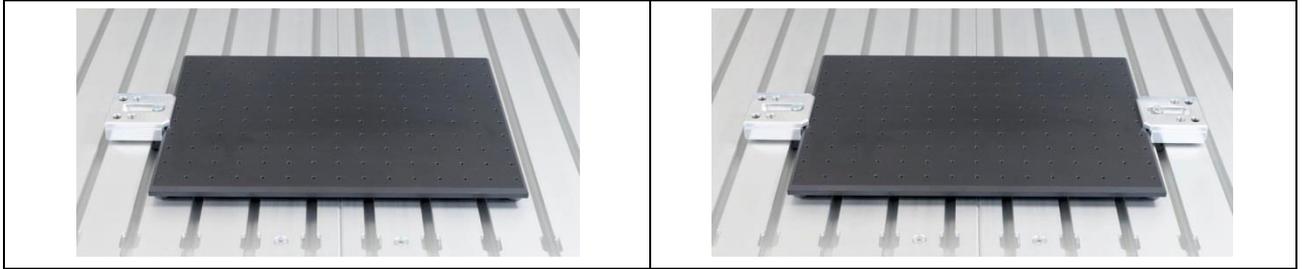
Befestigung des UH DUT mit den Spannpratzen auf dem T-Nutentisch
